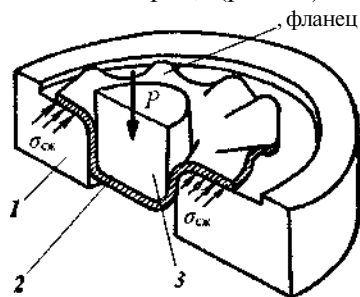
Образование складок при глубокой вытяжке: / - матрица; 2 - заготовка; 3 - пуансон
